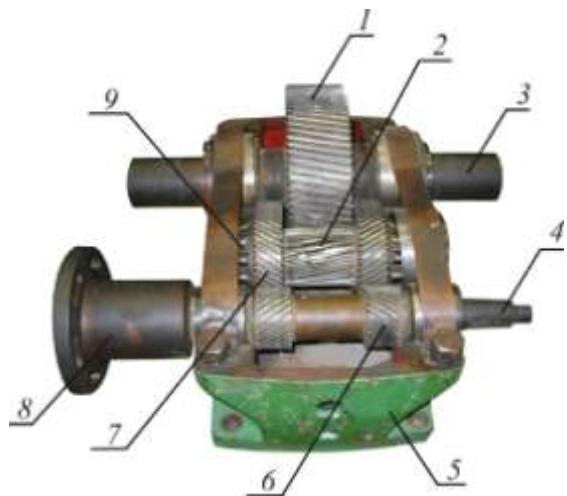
Редуктор двухступенчатый цилиндрический: 1, 7 — зубчатые колеса; 2, 6 — шестерни; 3, 4 — тихоходный и быстроходный валы; 5 — корпус; 8 — полумуфта; 9 — подшипник
